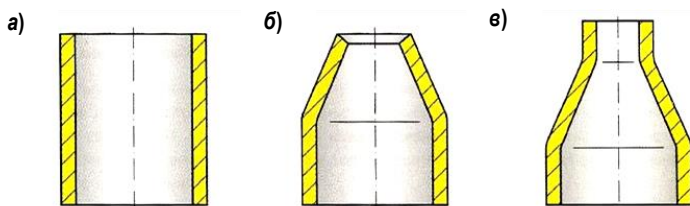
Операция обжима: а – заготовка; б – обжим на конус;
